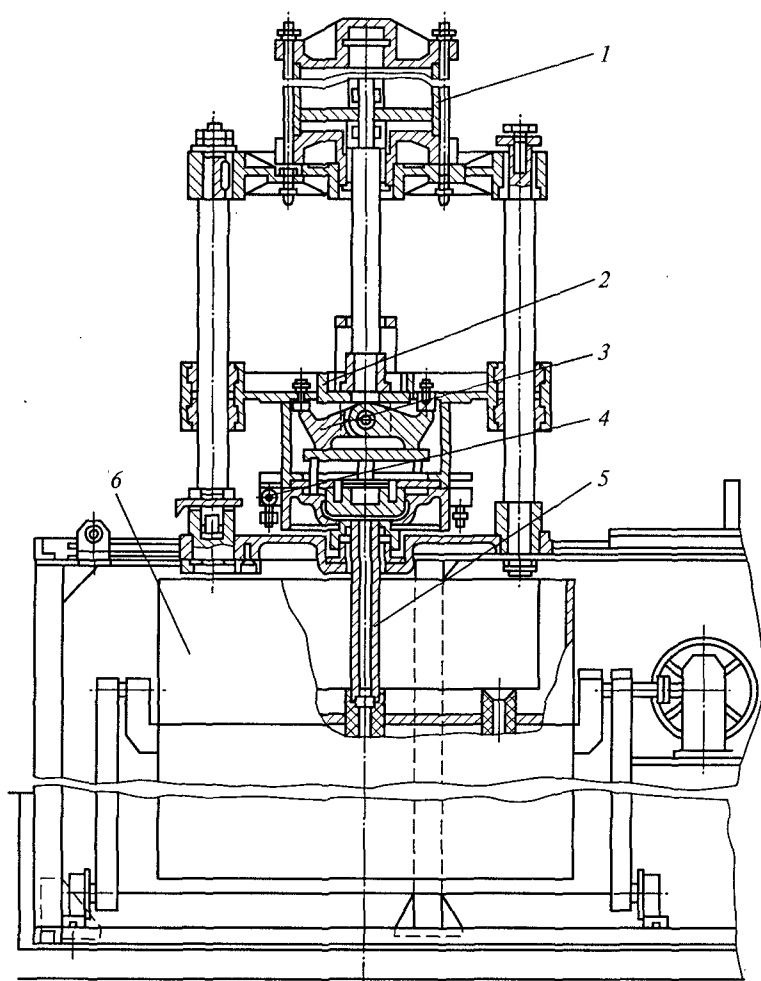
Установка модели ЛЭМД-002 для получения отливок из алюминиевых сплавов:
